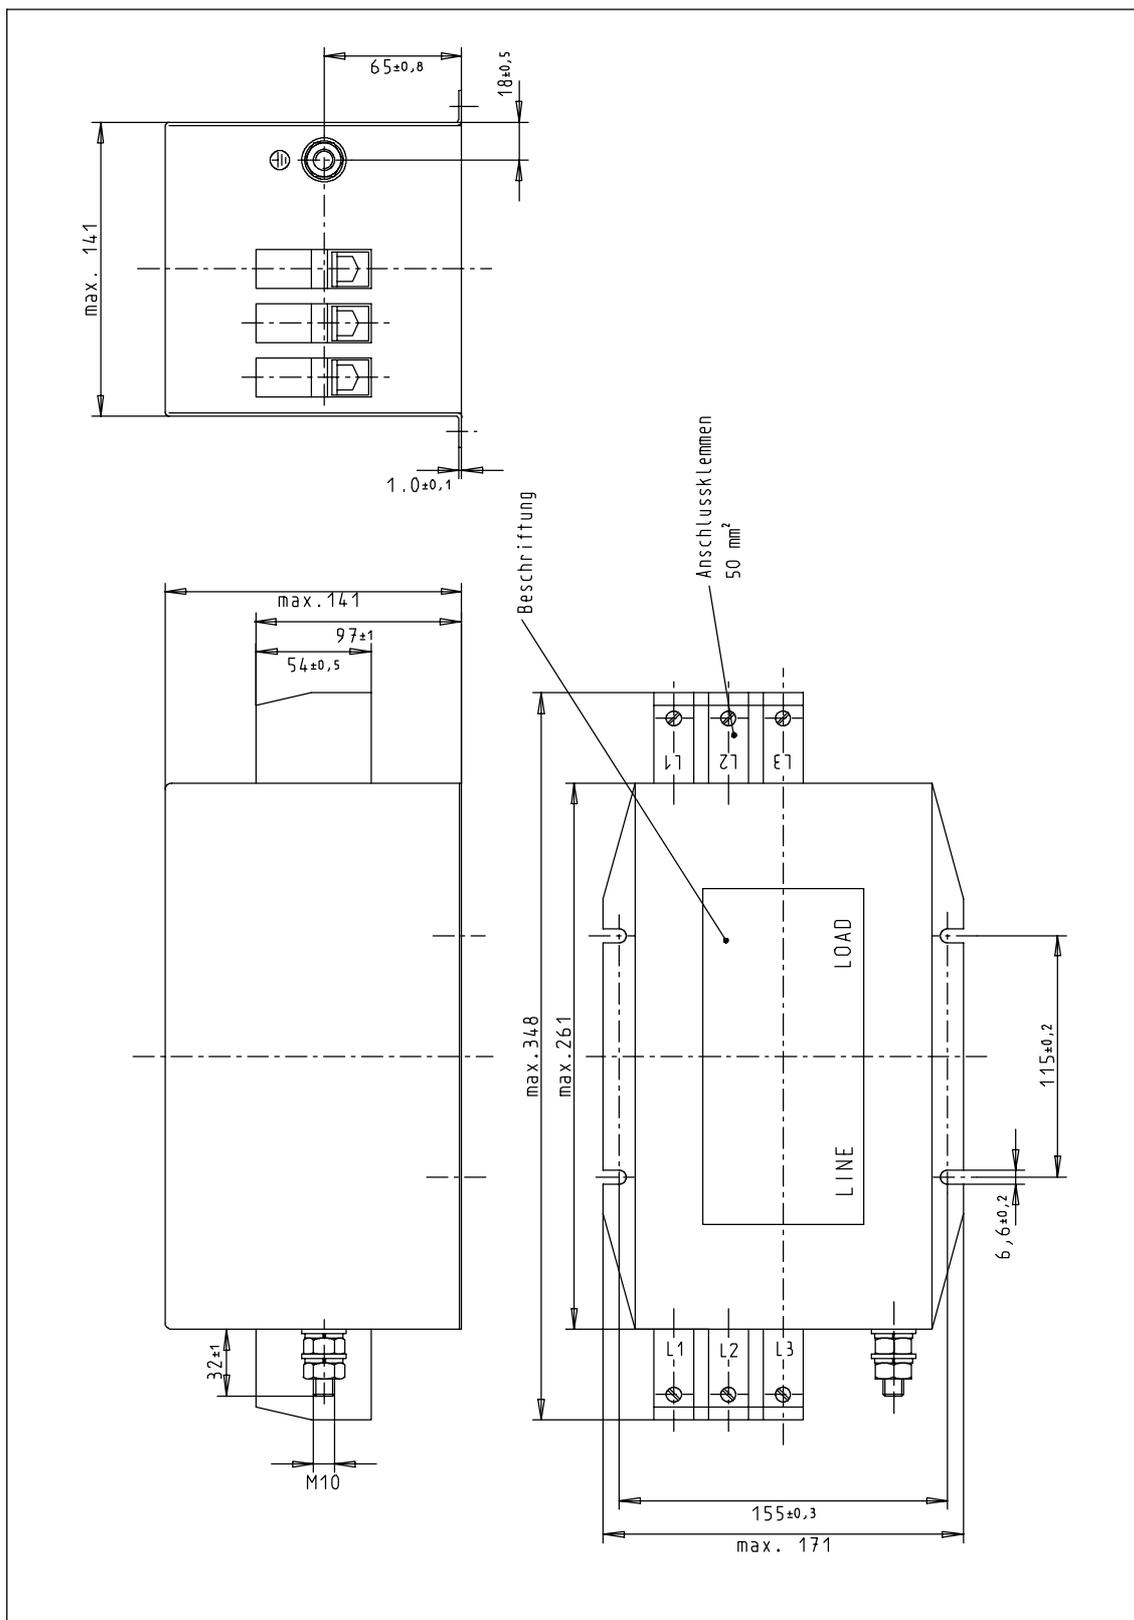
Filtro de red para módulos UE 28 kW, 6SN1111-0AA01-1CA1
